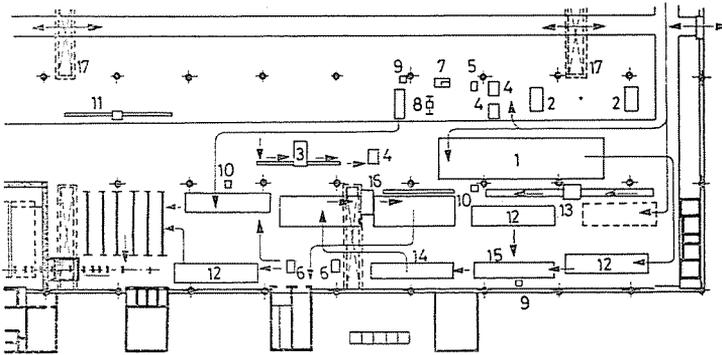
Fertigungstechnische Bearbeitungsreihe für Skelettsystem FEM-TIP: 1 Trennkreissäge; 2 Blechscherer; 3 Trennsäge mit Kunststoffscheibe; 4 Exzenterpresse; 5 Säulenbohrmaschine; 6 Radialbohrmaschine; 7 Tischbohrmaschine; 8 Gestell; 9 Schweißdynamo; 10 CO₂-Schutzgasschweißung; 11 Schneidbrenner; 12 Schlosser, Montageschlosser; 13 Biegerollgang; 14 Unter-Pulver-Schweißautomat; 15 Balkenzusammenbau; 16 Kreissäge mit senkrechtem Vorschub; 19 Elektrolaufkran
